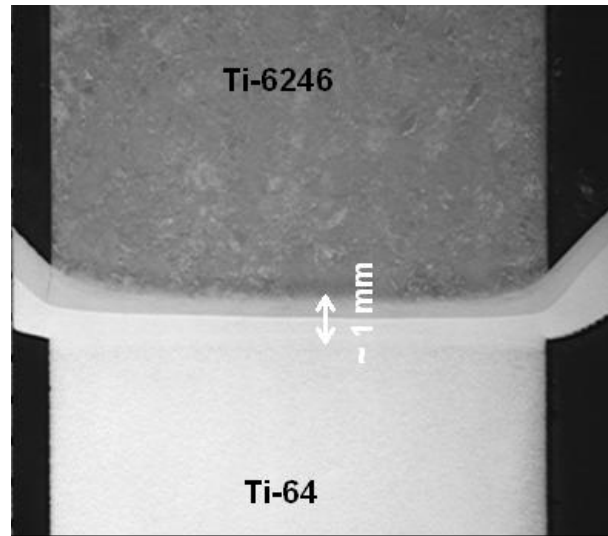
Macrografía de la unión soldada Ti-6246 + Ti-64
